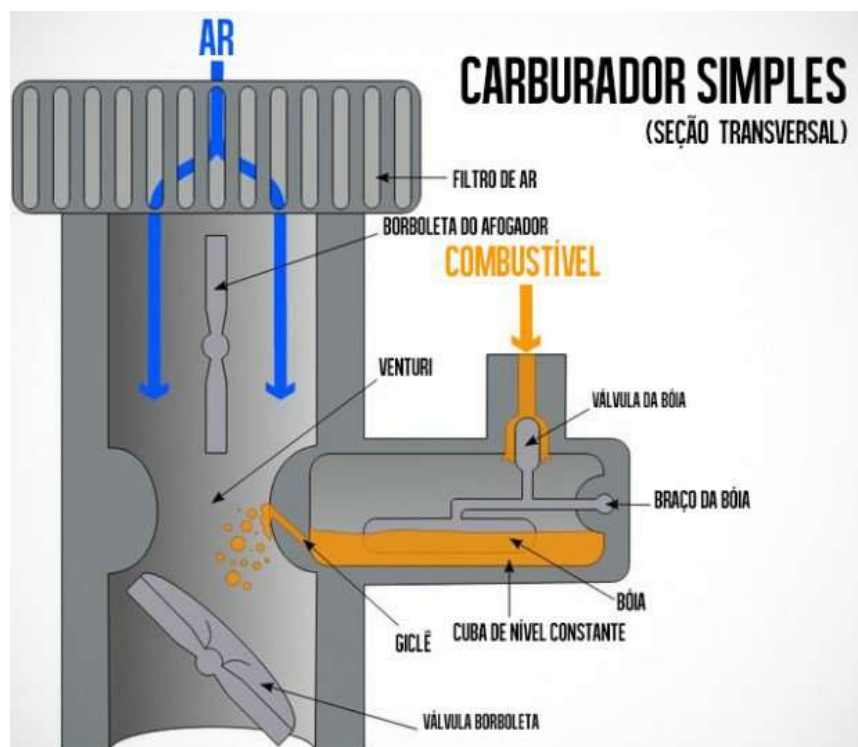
corte transversal de um carburador. Fonte: CONTESINI; 2014.
